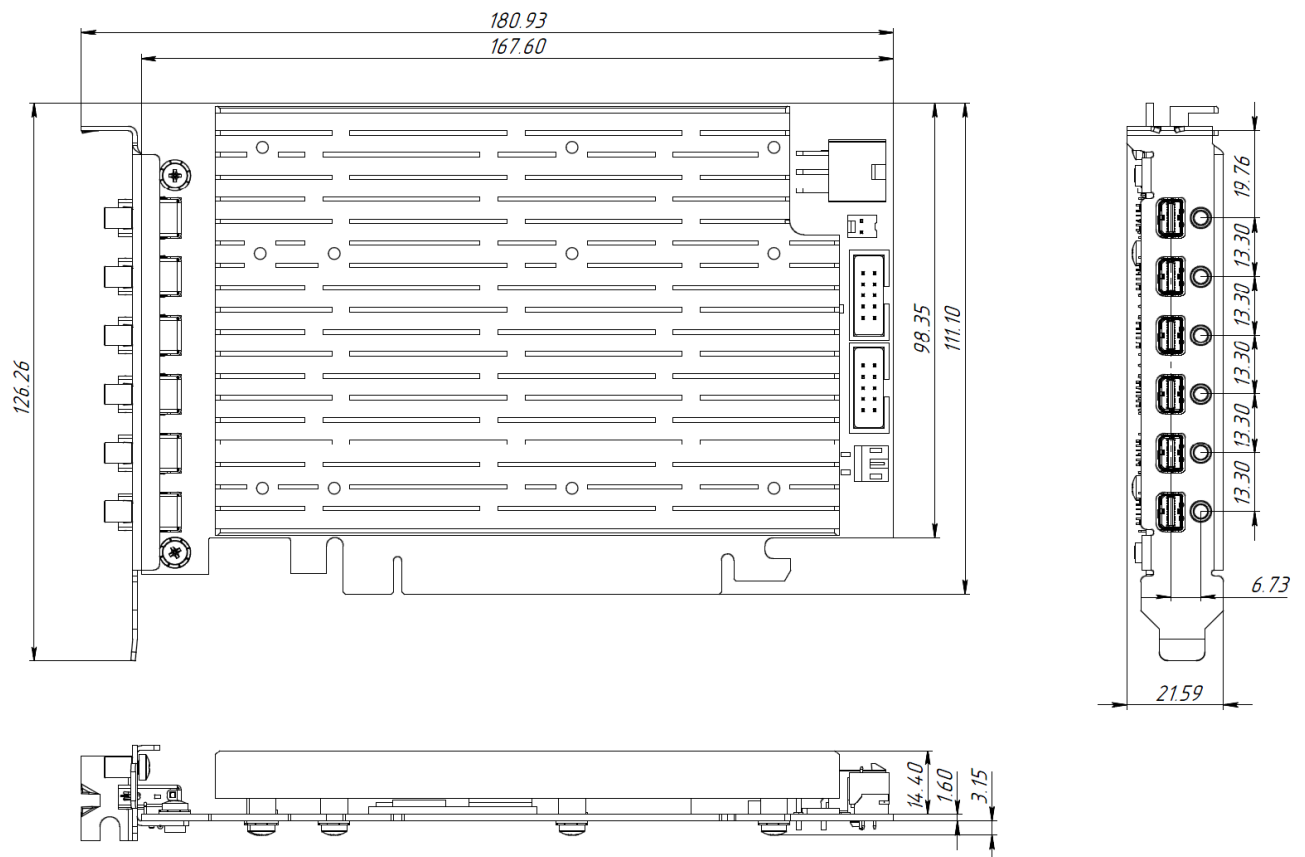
Чертеж внешнего вида для конфигурации "-02"
